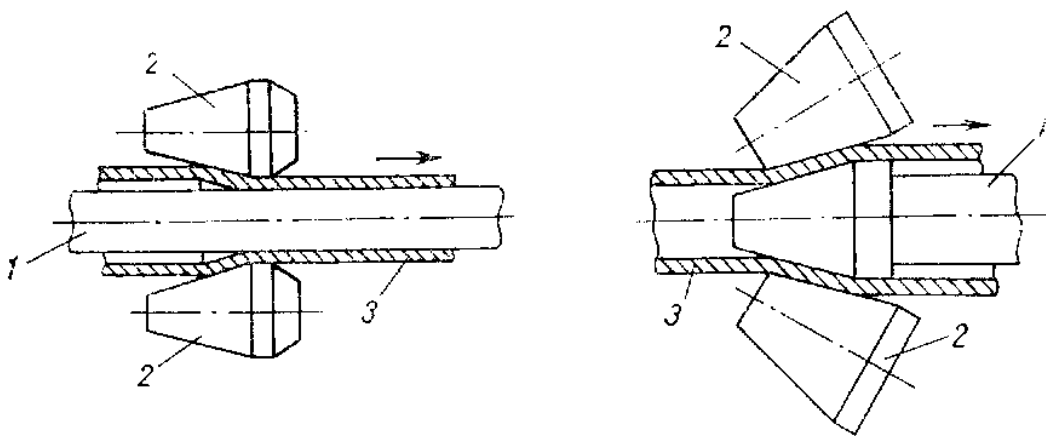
Схеми поперечного прокатування трубчастих заготовок на циліндричній та конічній оправках:
